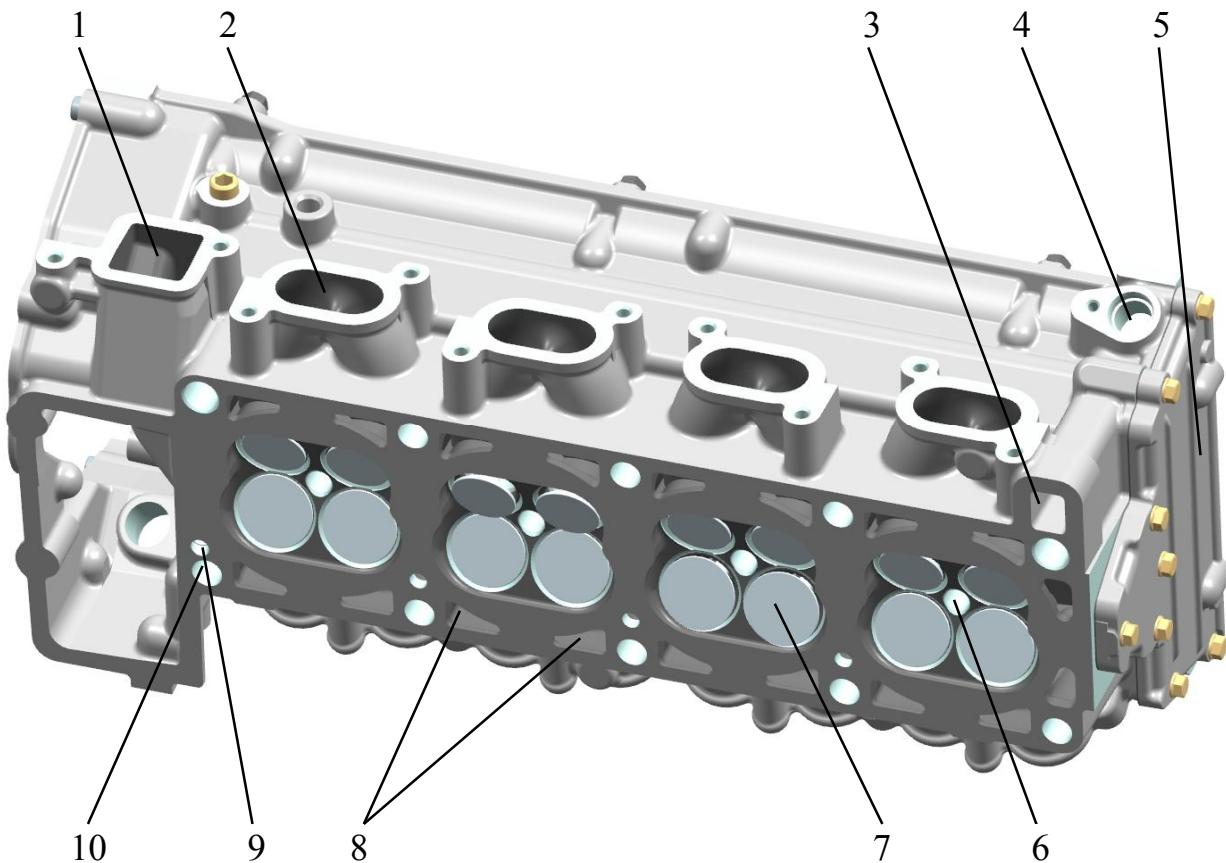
Головка цилиндров. Вид на камеры сгорания, фланец выпускного коллектора и заднюю крышку:
